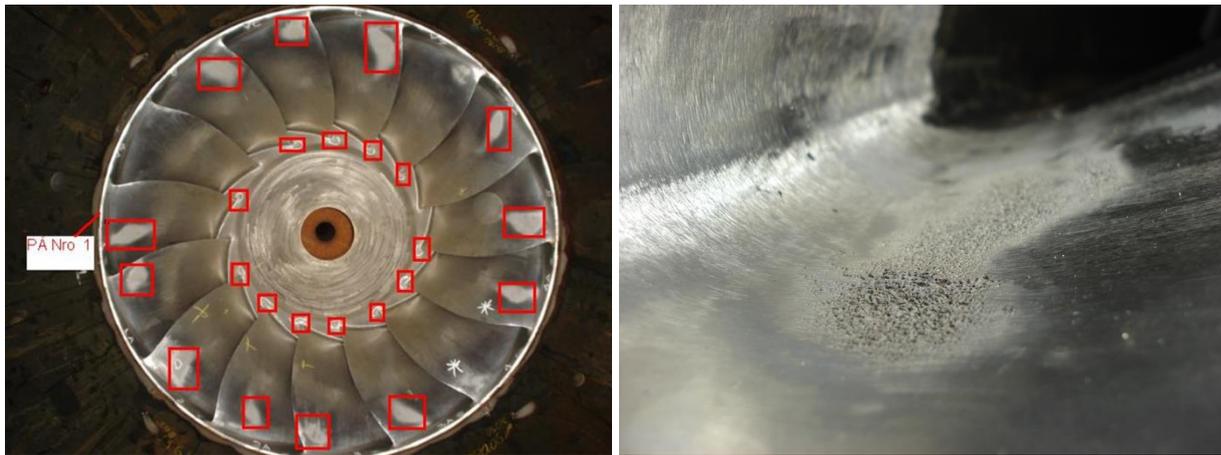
Desgaste cavitacional identificado na inspeção do rotor
